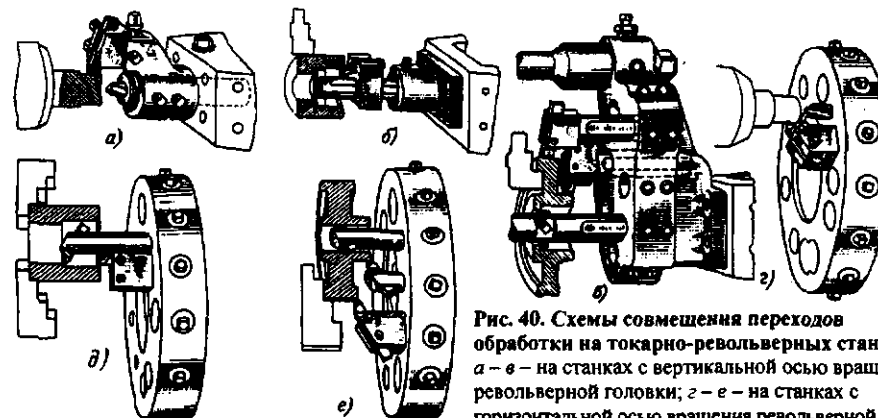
Схемы совмещения переходов обработки на токарно-револьверных станках: а – в – на станках с вертикальной осью вращения револьверной головки; с – е – на станках с горизонтальной осью вращения револьверной головки
